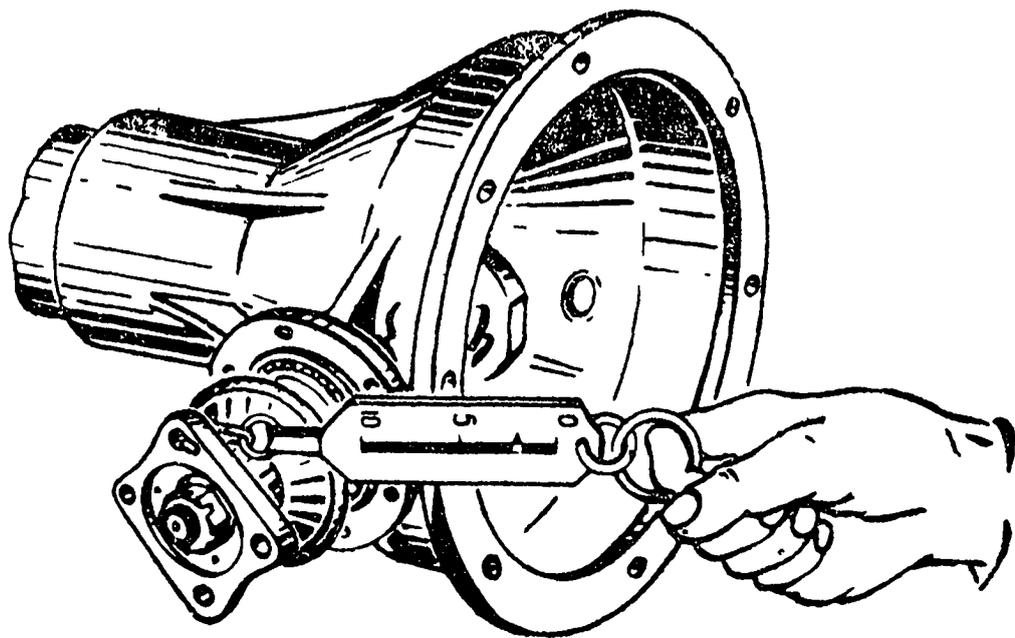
Проверка затяжки подшипников ведущей шестерни.
